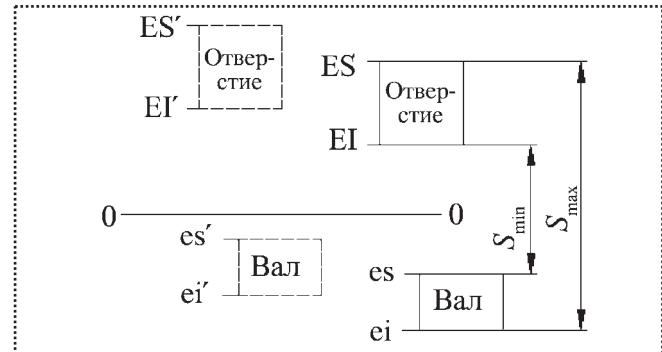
Произвольное расположение полей допусков размеров сопрягаемых поверхностей
